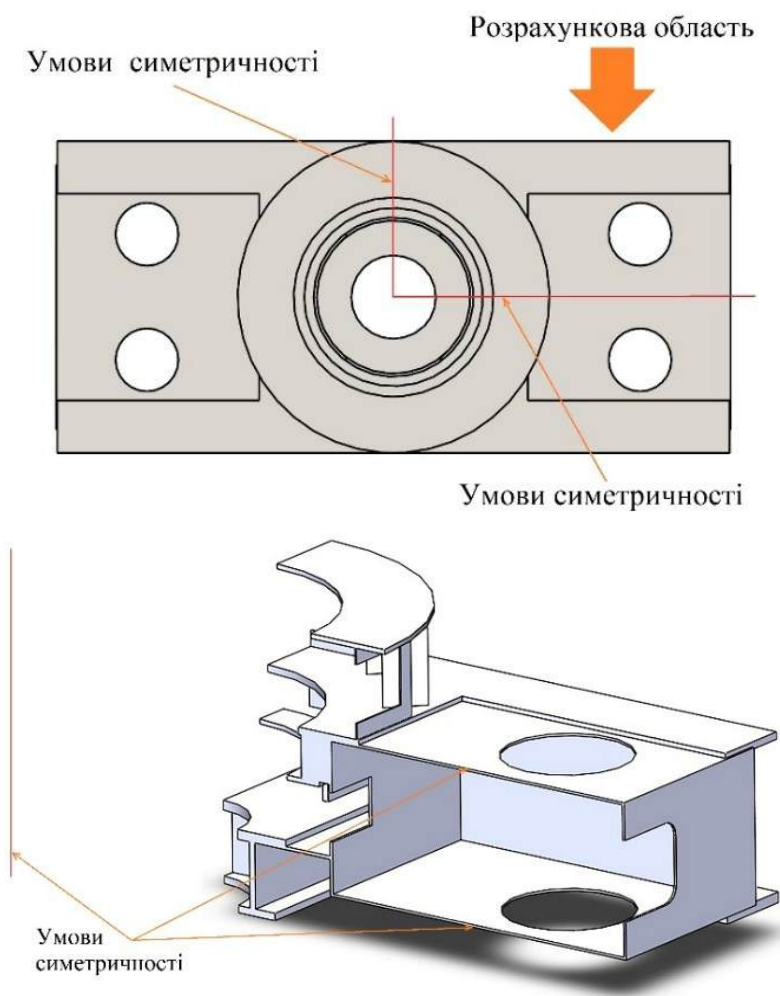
Розрахункова область існуючої верхньої хрестовини
